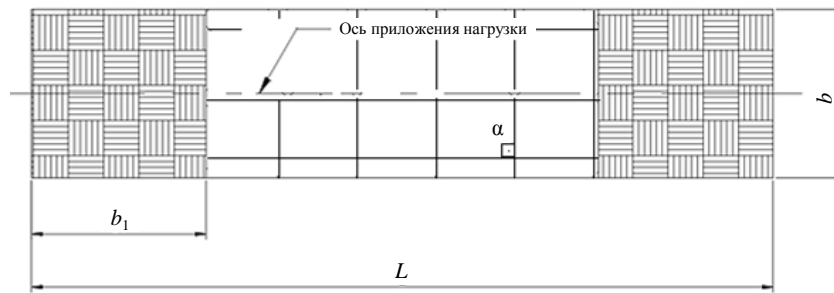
Схематическое изображение образца стеклопластика с конструктивной укладкой: α – угол укладки армирующего наполнителя; L – длина образца; b – ширина образца; b_1 – длина зоны зажима
